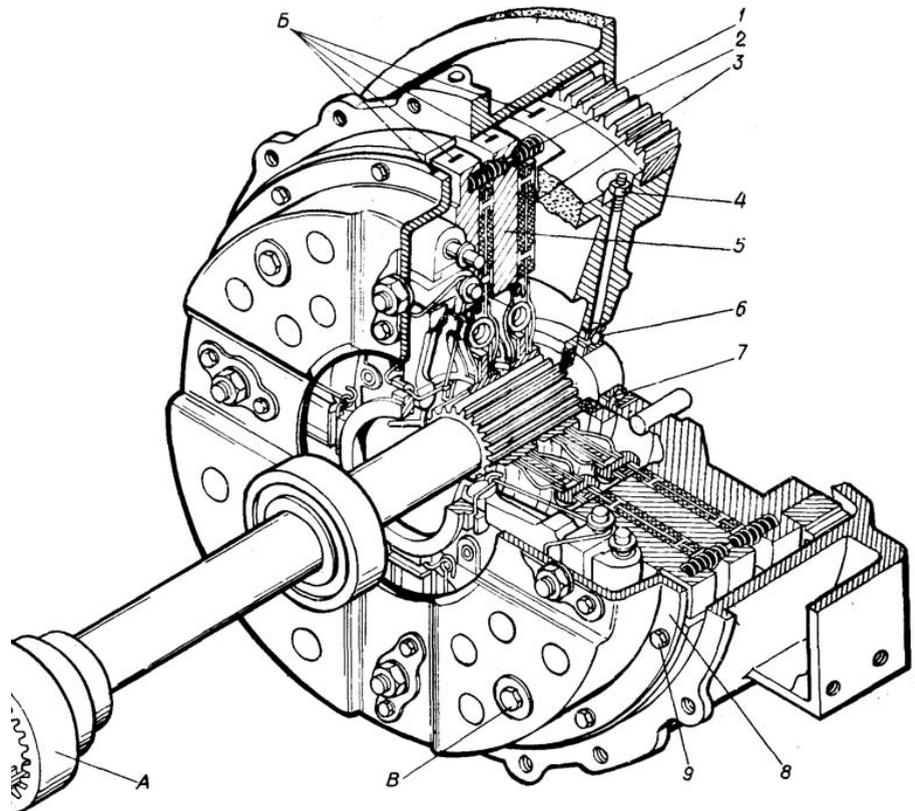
Сборка кожуха с корпусом сцепления: 1 — маховик; 2 — пружина; 3 — диск ведомый; 4 — масленка; 5 — диск промежуточный; 6 — подшипник; 7 — манжета; 8 — кожух; 9 — болт; А — вал технологический; Б — метка; В — болт технологический
